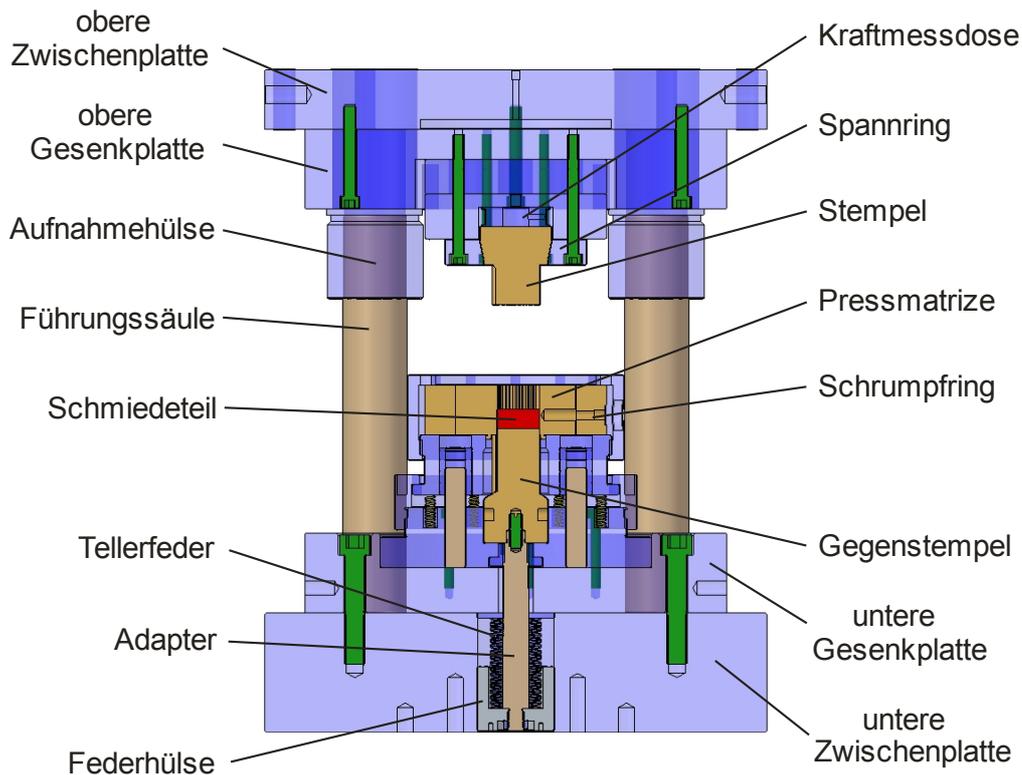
CAD-Querschnitt des Werkzeugsystems
